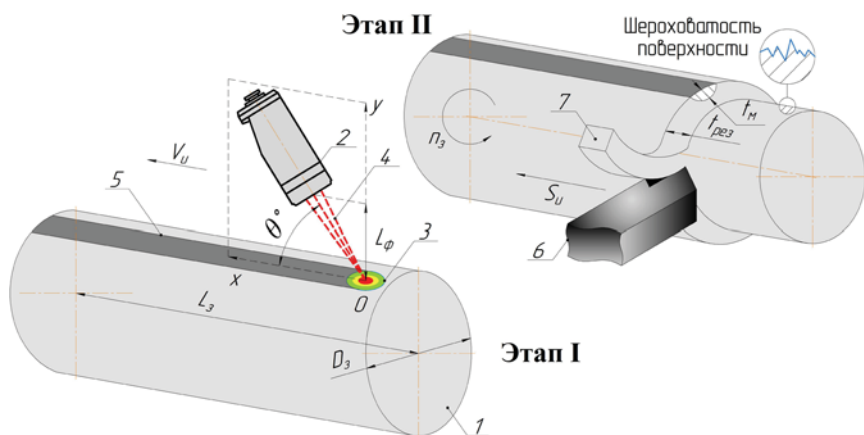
Метод управляемой сегментированной механической обработки: 1 – заготовка; 2 – лазерная головка; 3 – диаметр лазерного пятна; 4 – лазерное излучение; 5 – сегментированная зона с модернизированной структурой; 6 – режущий инструмент; 7 – процесс стружкообразования
